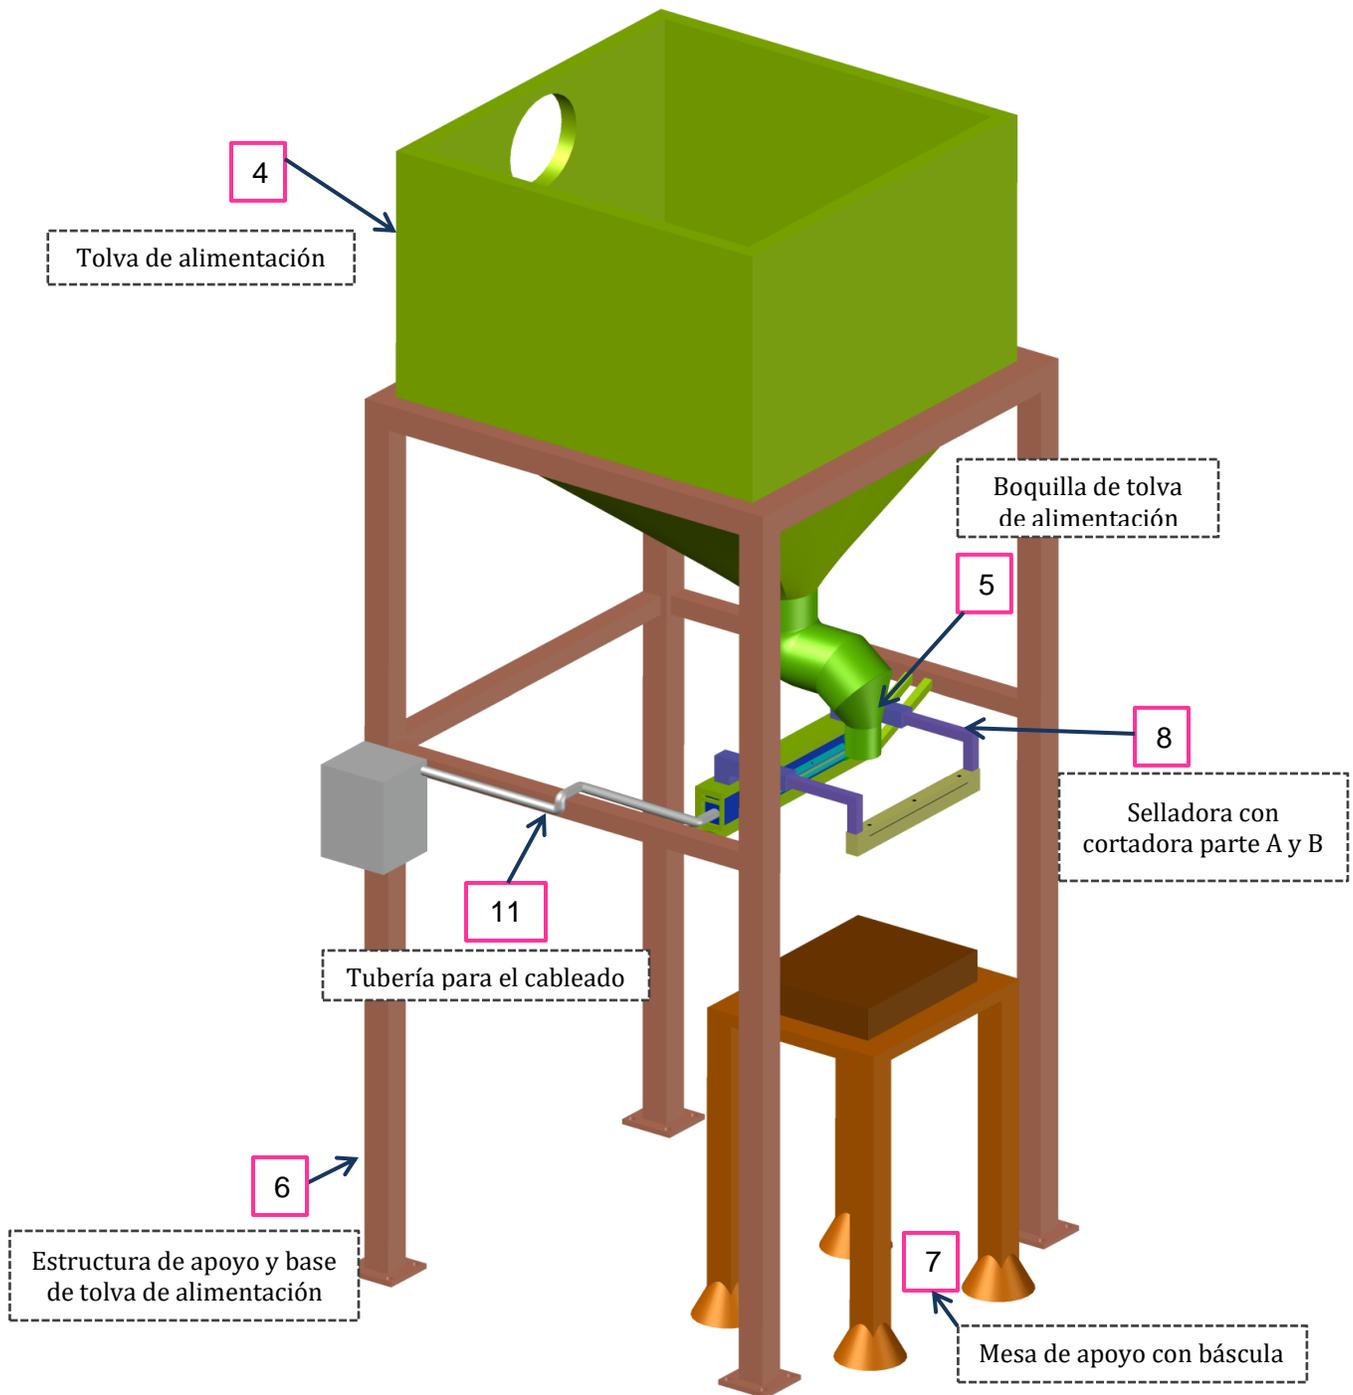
Prototipo parte de llenado ensamblado – parte principal del prototipo
